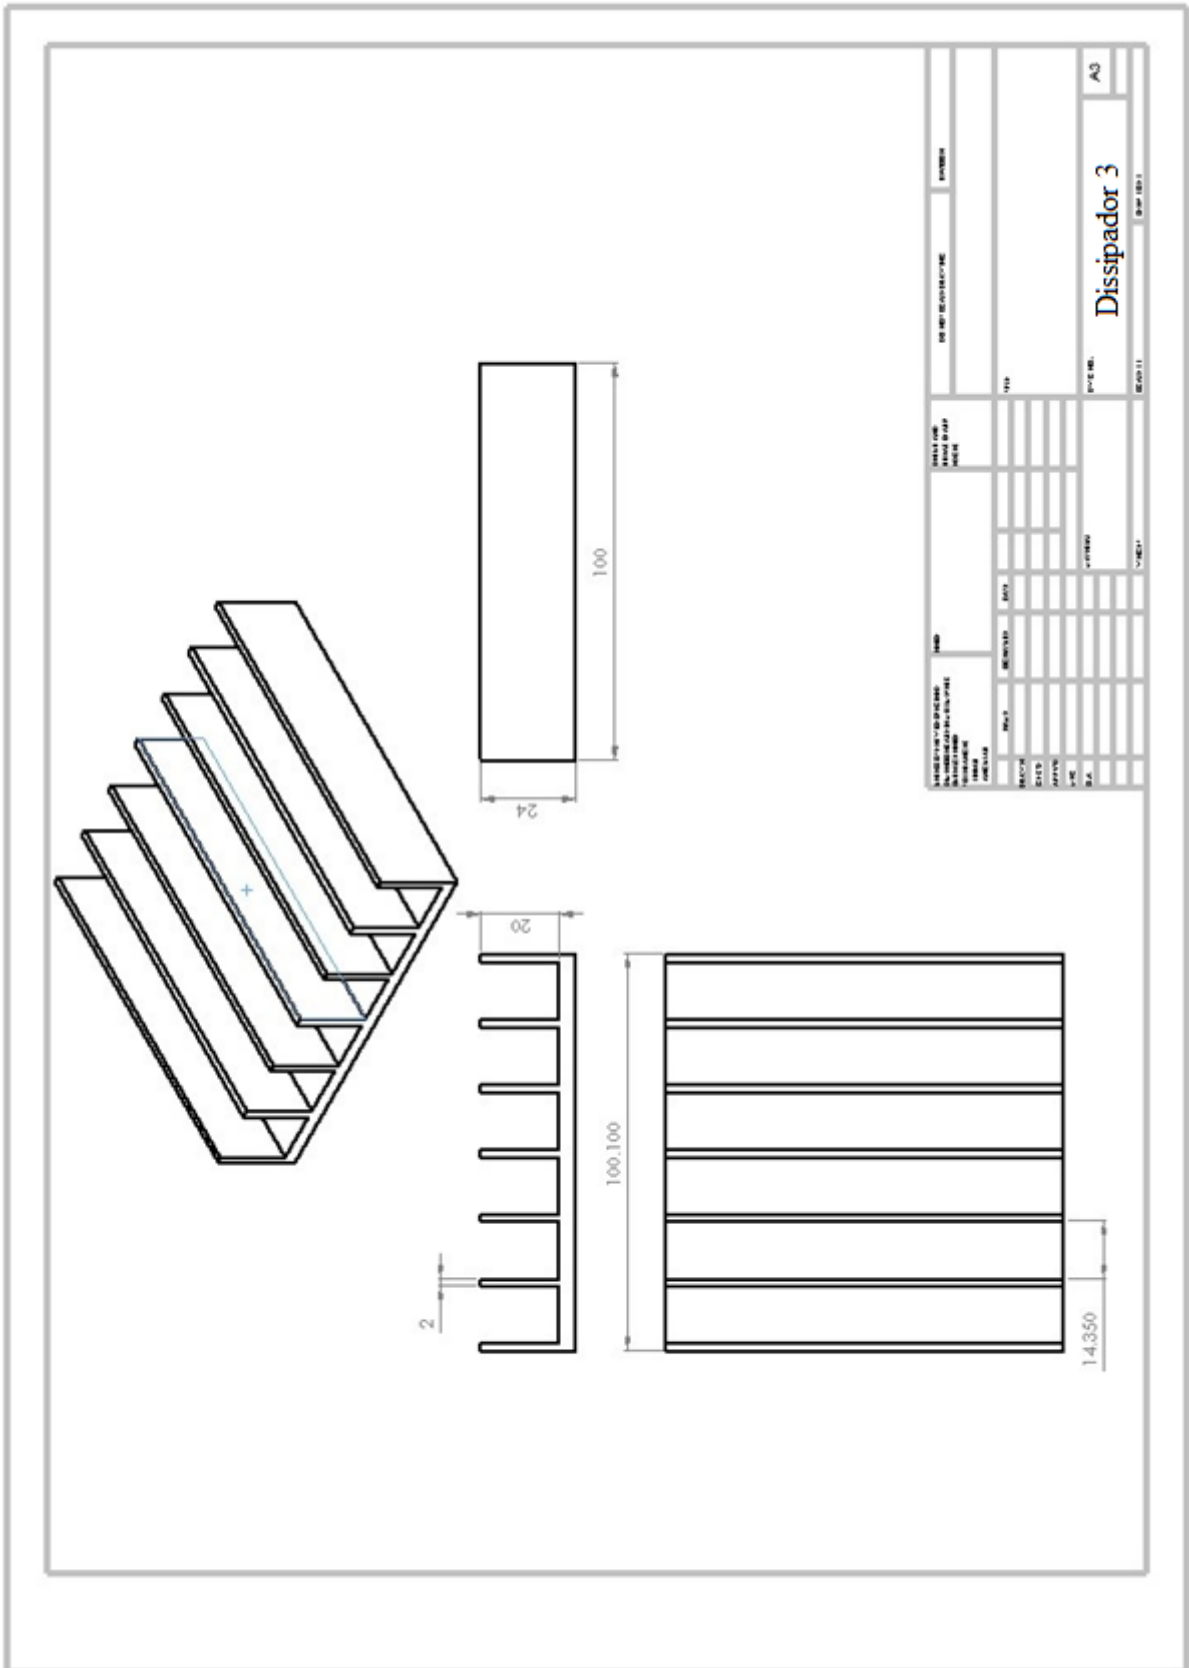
Desenho técnico utilizado para confecção do Dissipador 3.
